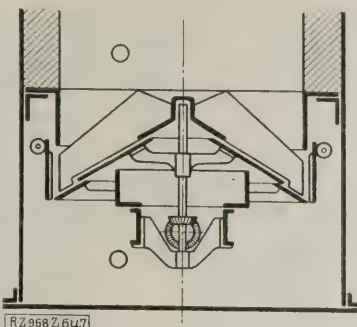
Gaserzeuger von Müller, DRP 87 444.
